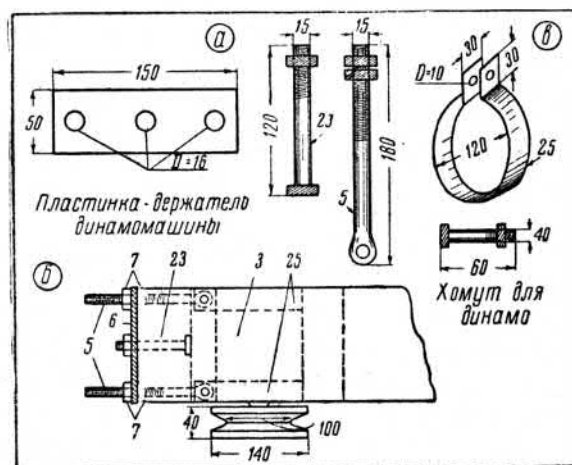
Детали для крепления динамомашин: а — пластинка-держатель, б — расположение деталей в головке двигателя, в — хомут и болты
